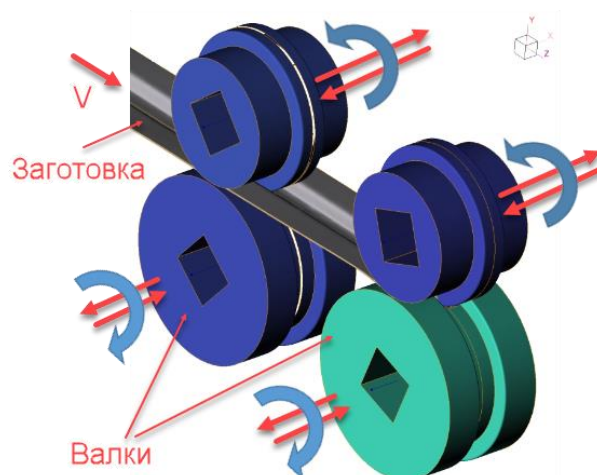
3D-моделі валків двох останніх клітей (стрілками позначені напрями обертання та руху заготовки)
